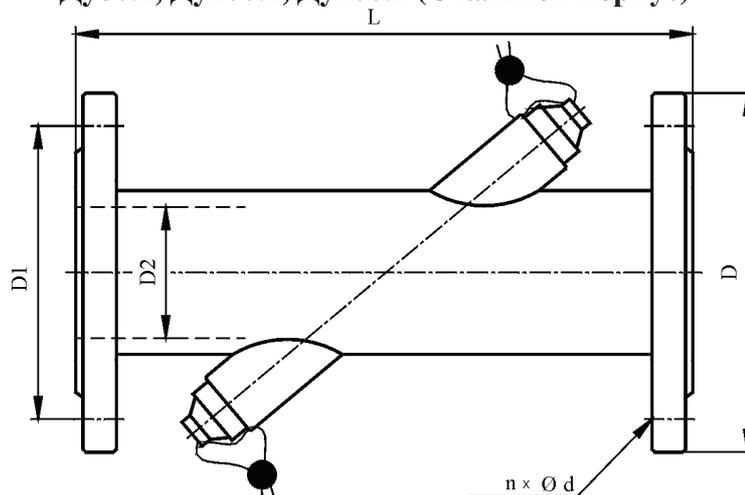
Габаритные размеры ультразвукового преобразователя расхода с Ду50, Ду50.1, Ду65, Ду65.1, Ду80, Ду80.1, Ду100.1, Ду100.2 (Латунный корпус)
